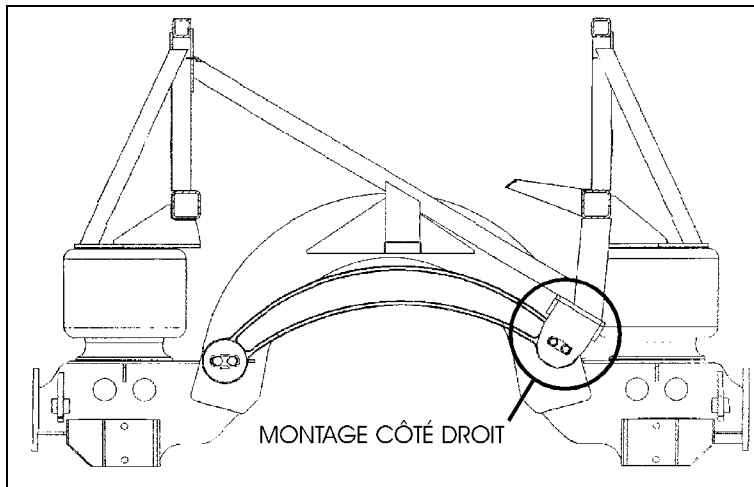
ESSIEU AUXILIAIRE - VUE DE L'ARRIÈRE
